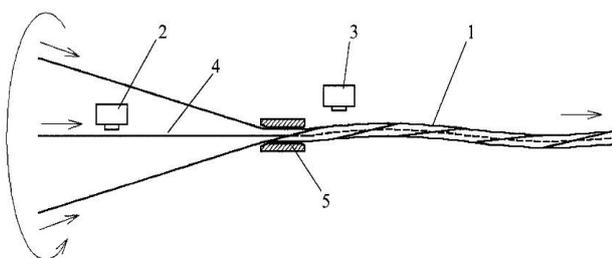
Контроль параметров свивки каната при изготовлении (1 – канат; 2, 3 – датчики контроля длины; 4 – металлический сердечник; 5 обжимная плашка)
